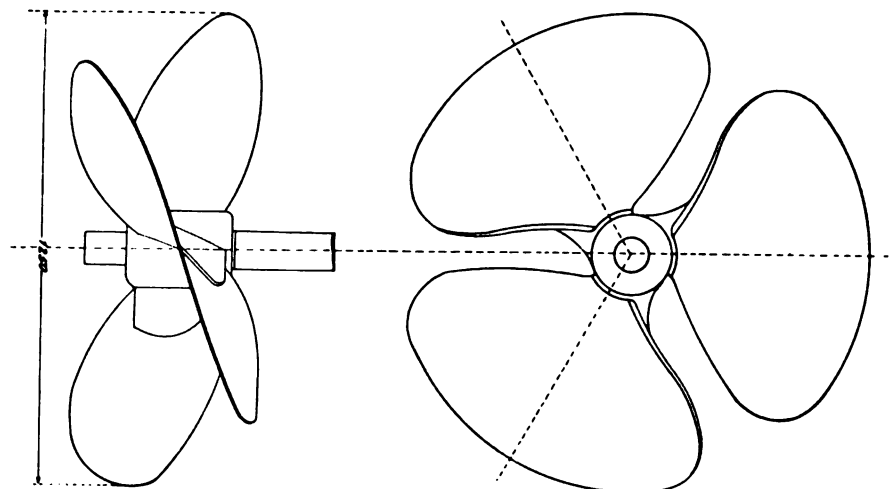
Breitflügelige Schraube für einen 100 PS starken Schleppdampfer. 1:20.
